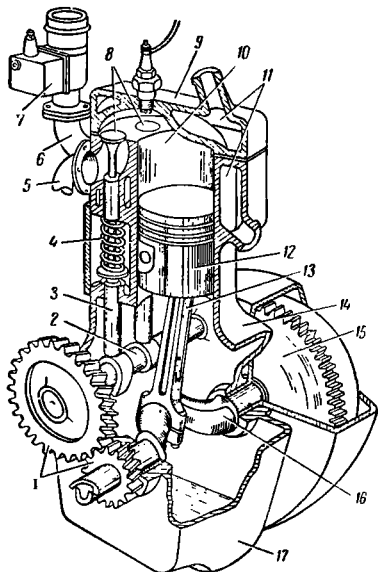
Схема устройства одноцилиндрового карбюраторного двигателя.
